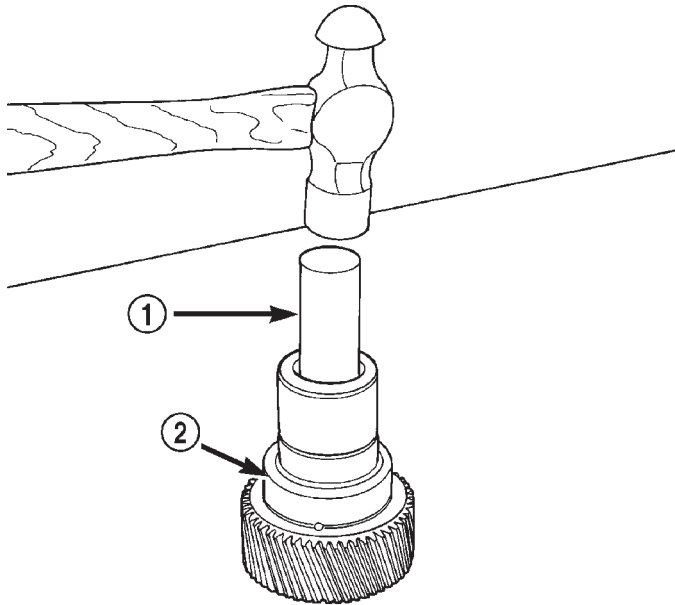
Asentamiento del cojinete del engranaje impulsor
